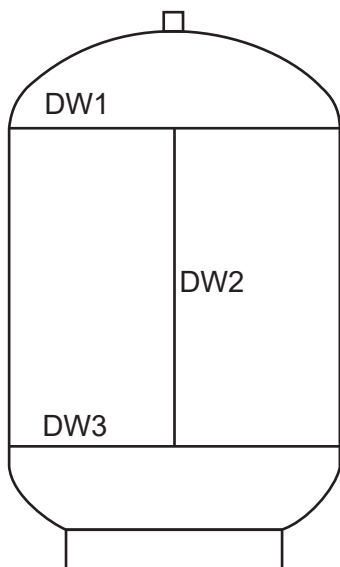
Обозначение сварного соединения (тип 2)
